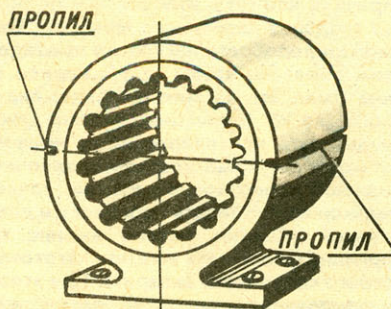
Подготовительные операции для извлечения статора из корпуса электродвигателя.
